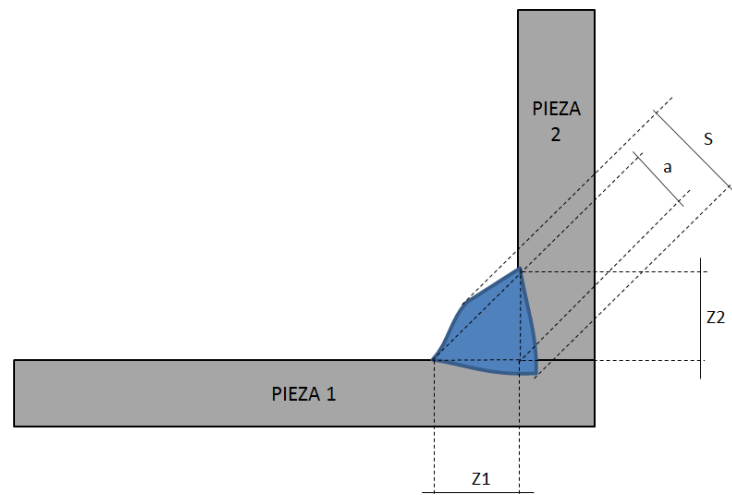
Dimensiones de control en un cordón de soldadura.
